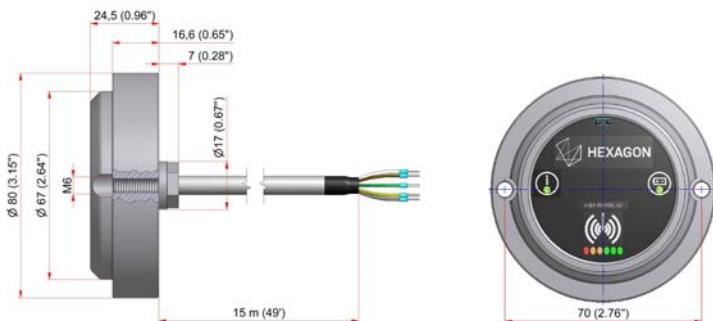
Dimensions RWR95.50-A (sortie axiale du câble)
